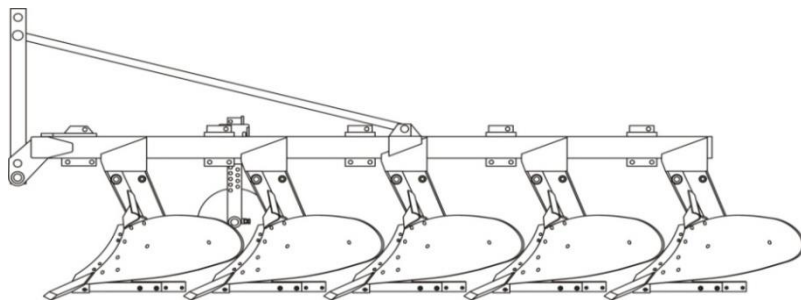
Общий вид плуга-рыхлителя с корпусами плужными «Д»
